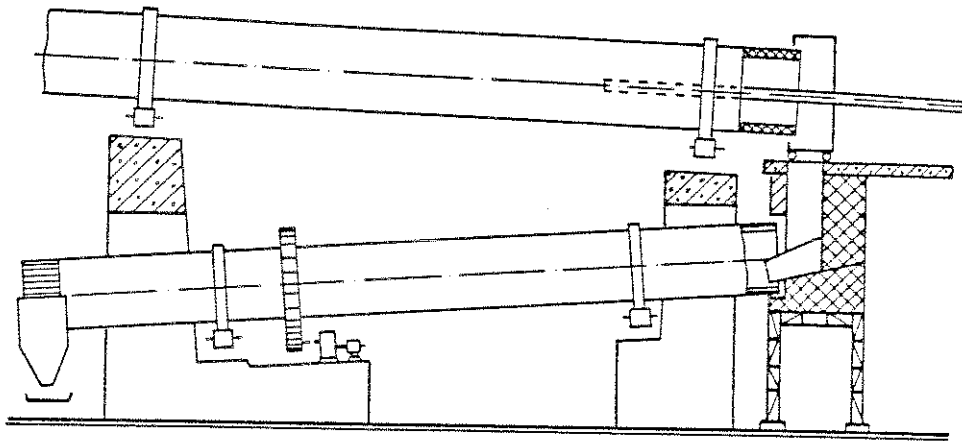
Längsschnitt durch Kühltrommel mit Drehofen
